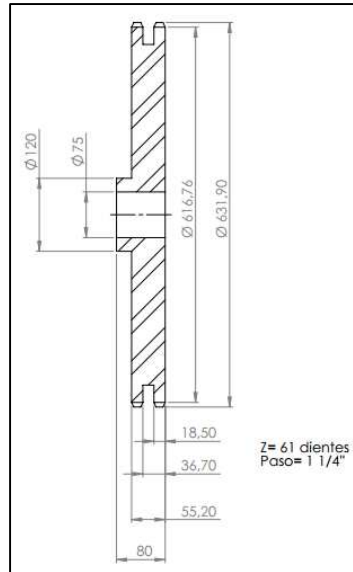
Engranaje doble de 61 dientes, paso 1 1/4"
